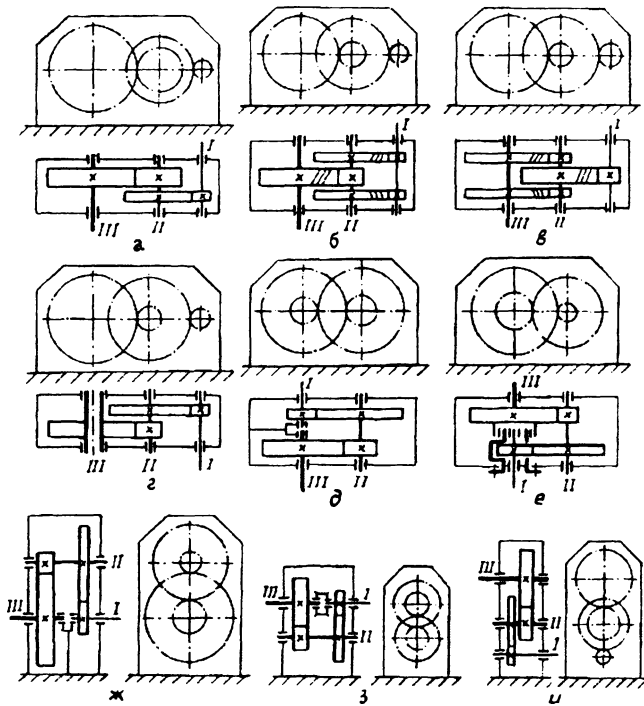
Кинематические схемы двухступенчатых цилиндрических редукторов по развернутой схеме (а...г, и) и соосных (д...з):
